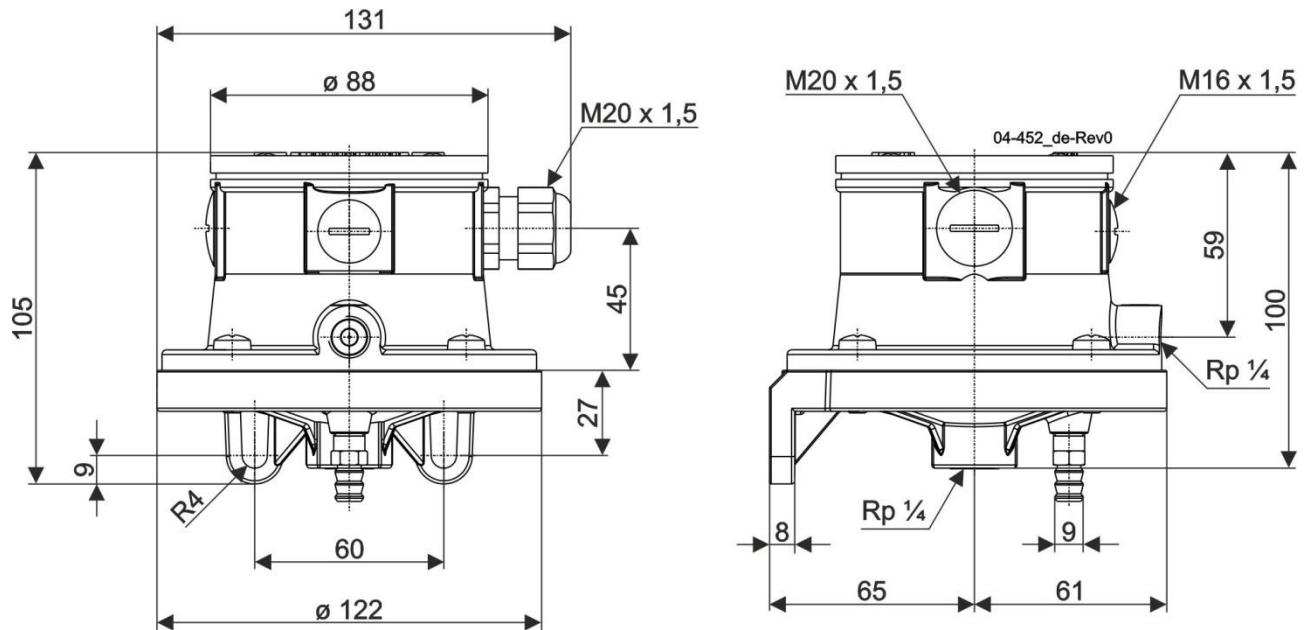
Maßblatt Druckwächter (Ausführung mit Verschlusschraube und Kabelverschraubung)
